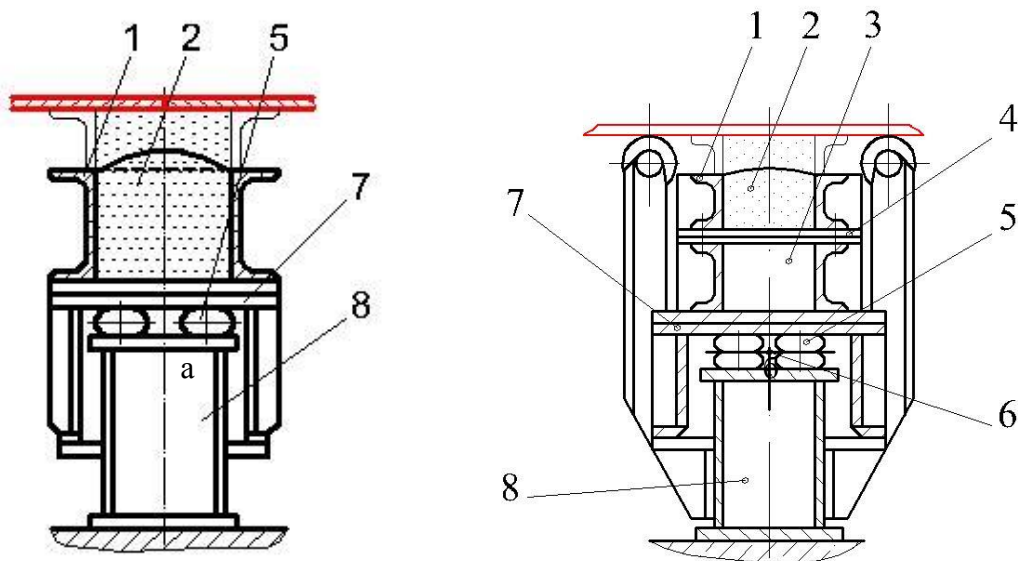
Основные типы подъёмных флюсовых подушек для сварки прямолинейных стыковых соединений листовых полотнищ:
